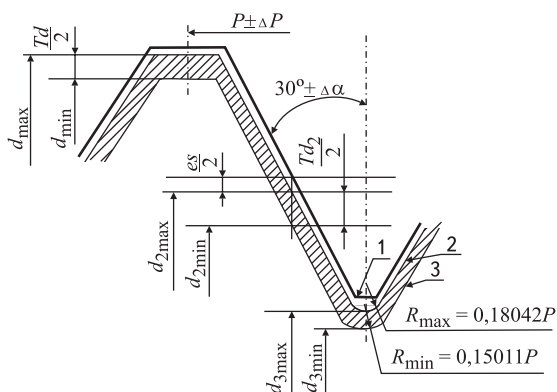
Предельные профили наружной резьбы: 1 — основного профиля; 2 — максимальный профиль; 3 — минимальный профиль
